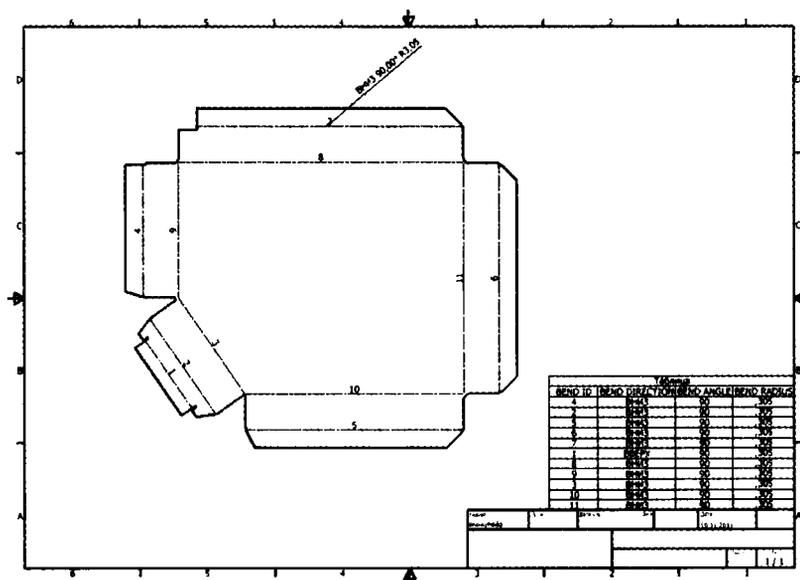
Таблица сгибов и развертка помещены на чертеж
